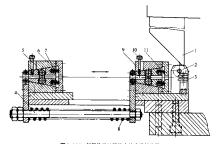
斜機传动的液柱夹持式送料装置 1—斜模; 2—滚轮; 3—导料轮; 4—螺杆; 5—液柱; 6—止退火持器; 7、8—弹簧; 9—送料夹持器; 10—手柄; 11—滚柱保持架
